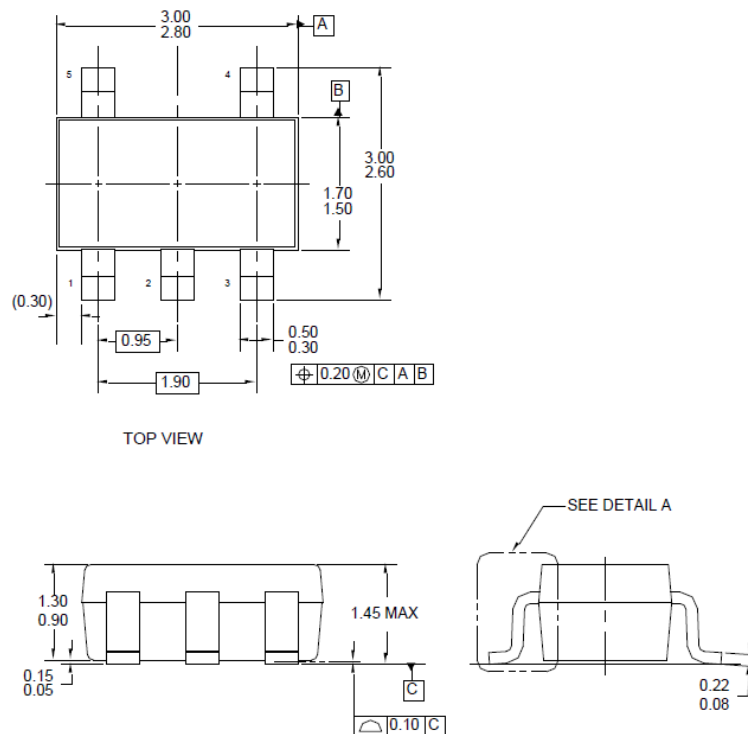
Зовнішній вигляд та габаритні розміри КМОН-інвертора NC7Z04M5X в корпусі SOT-23-5
